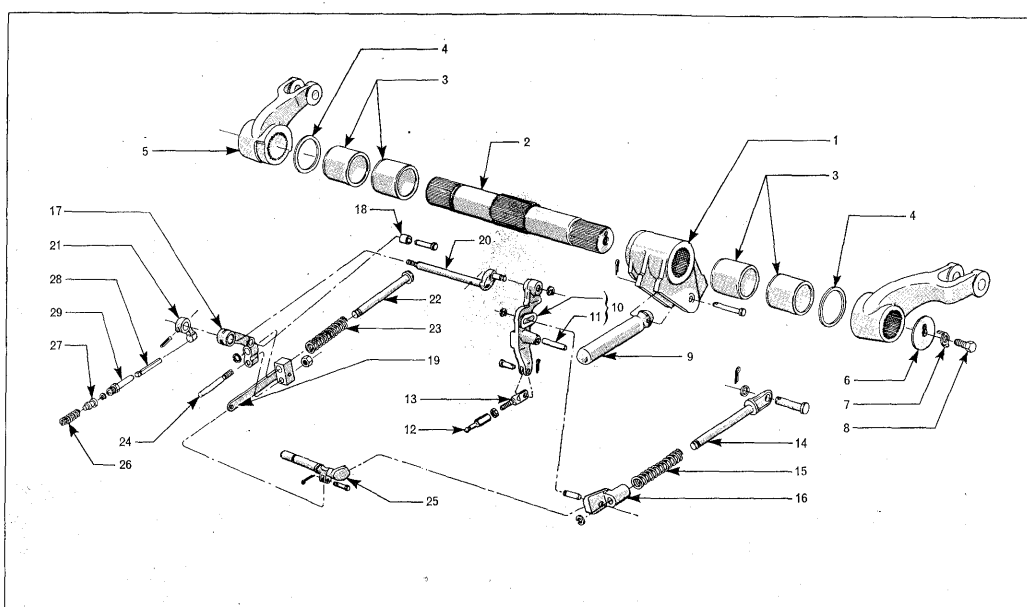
Exploded view af hydraulikkens interne mekanisme.
